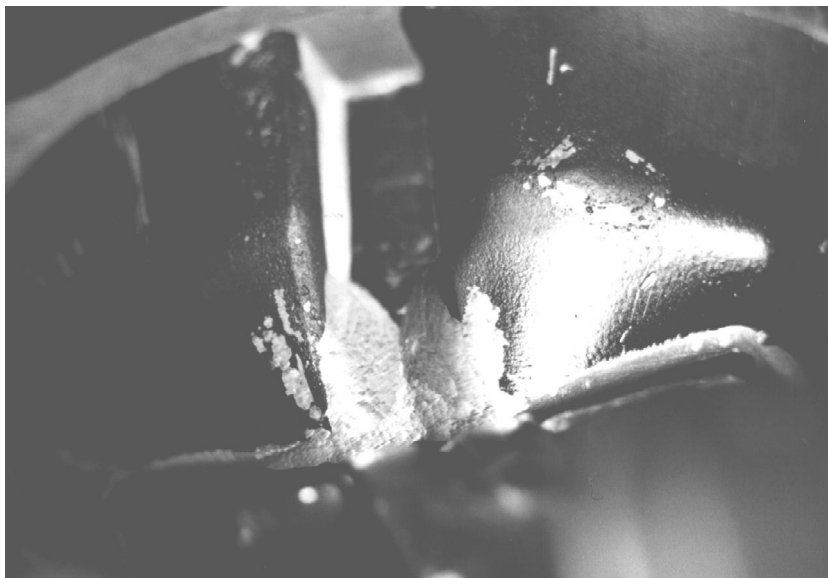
Bearbeiteter Steg im Kurbelgehäuse
